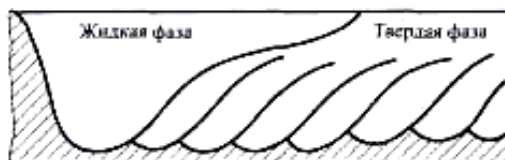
Форма шва в продольном сечении при лазерной сварке
